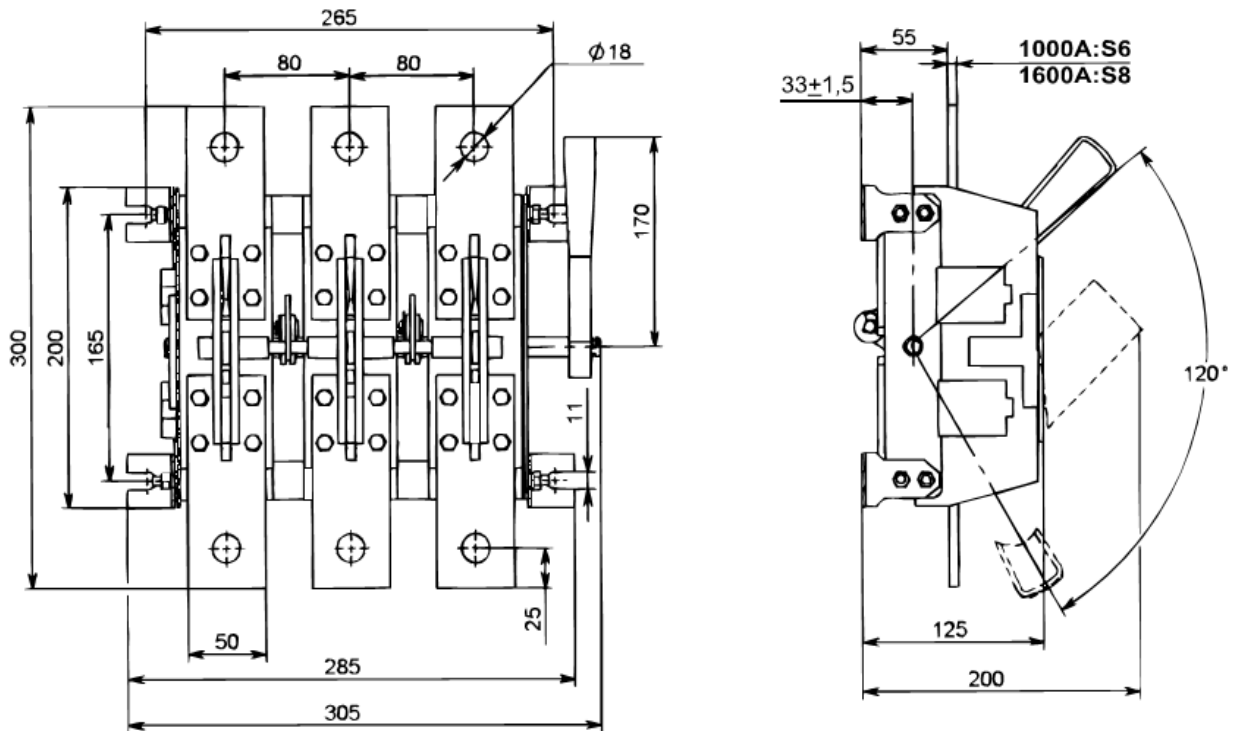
Разъединитель PE19 трехполюсный с боковой рукояткой, переднего присоединения шин
